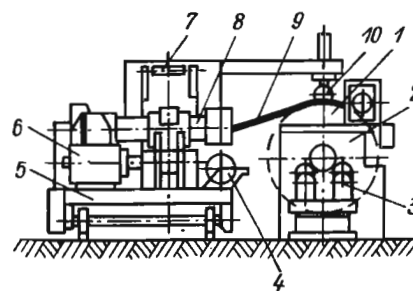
Схема установки для спирального наложения шприцованной ленты на поверхность вала:
